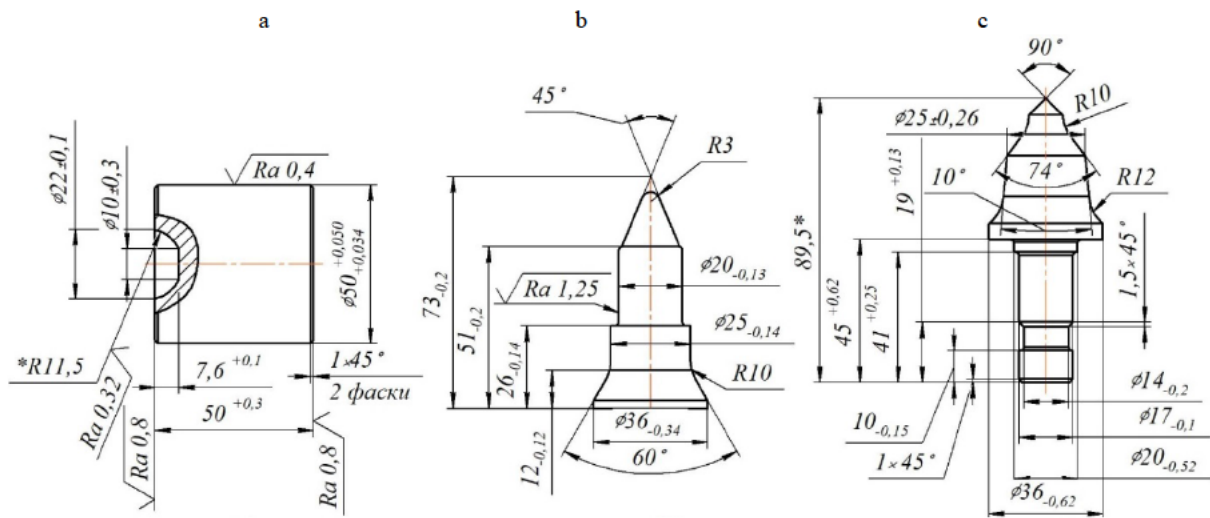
Детали-представители: а – вставка пуансона; б – прошивной пуансон; с – тангенциальный резец
